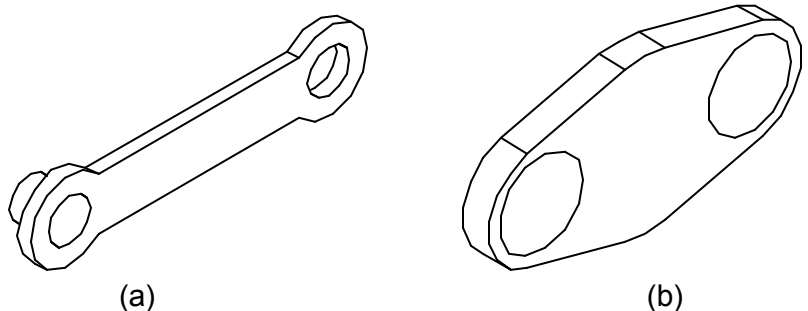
Benda Kerja Torak (a) dan dimensinya (b)
